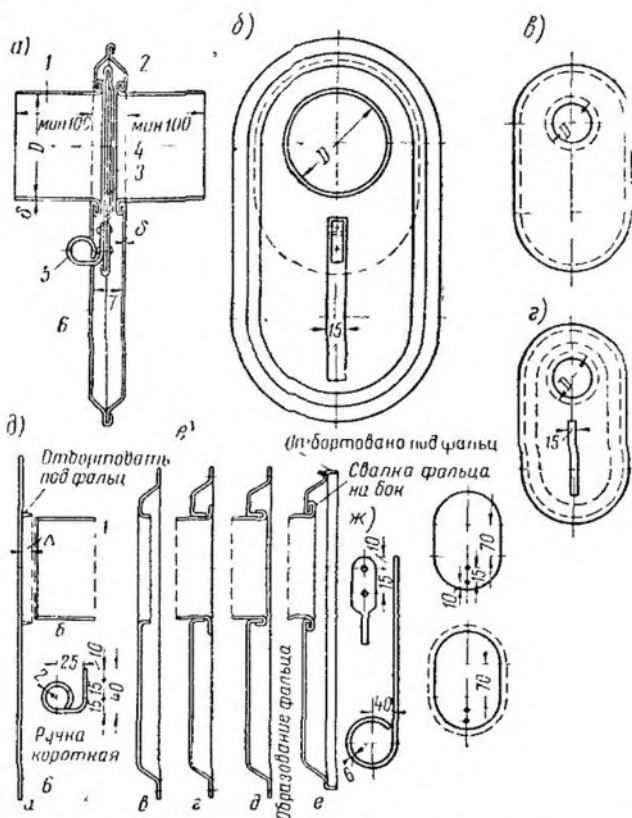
Изготовление шибера для воздуховодов диаметром до 500 мм
